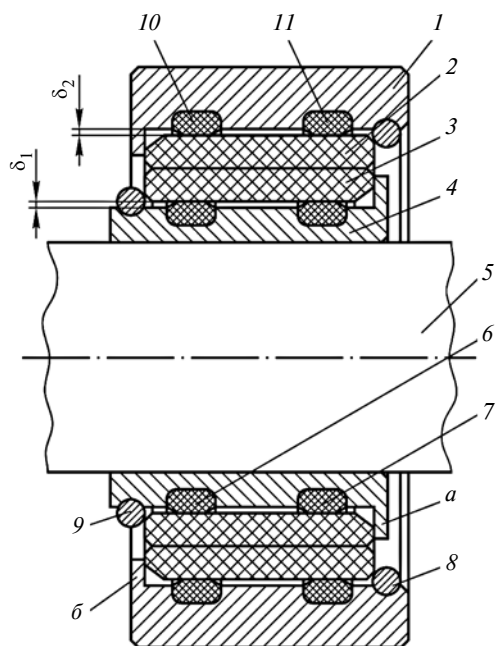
Радиальный подшипник скольжения с вкладышем из прессованных древесных секторов (поперечное сечение корпуса подшипника):
